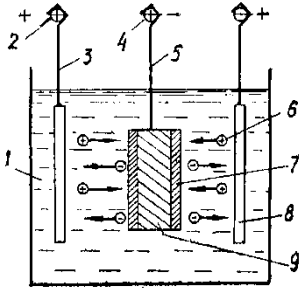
Схема електрохімічного осадження металу: 1 – ванна; 2 – анодна штанга; 3 – гак (підвіска) для навішування анода; 4 – катодна штанга; 5 – гак (підвіска) для завішування деталі (катоду); 6 – іони металу (катіони  $Me^{n+}$ ); 7 – покриття ( $Me_0$ ); 8 – анод; 9 – деталь (катод)
